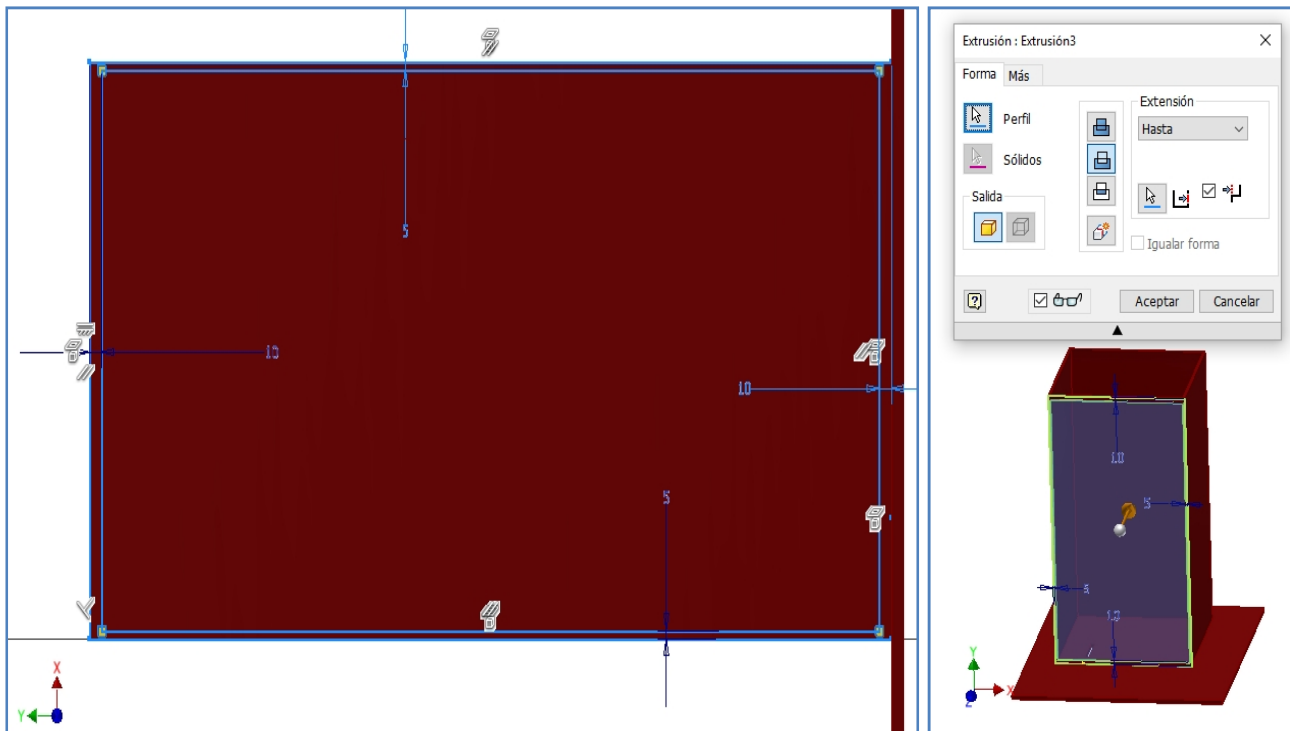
A. Boceto 3 para realizar vaciado para marco o extrusión 3- Izquierda. Figura 4.9.B. Extrusión del marco- Derecha.
